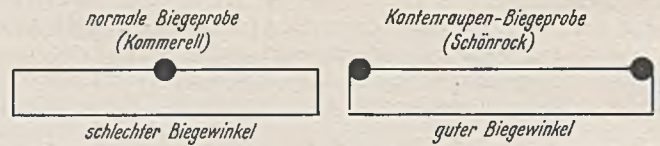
Einfluß der Lage der Schweißraupe auf den Biegewinkel bei der Schweißraupenbiegeprobe.
